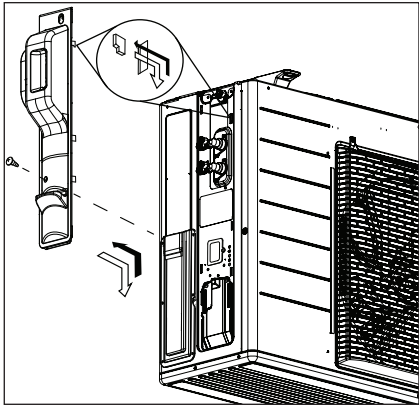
Retirer le couvercle principal pour accéder au deuxième couvercle.
